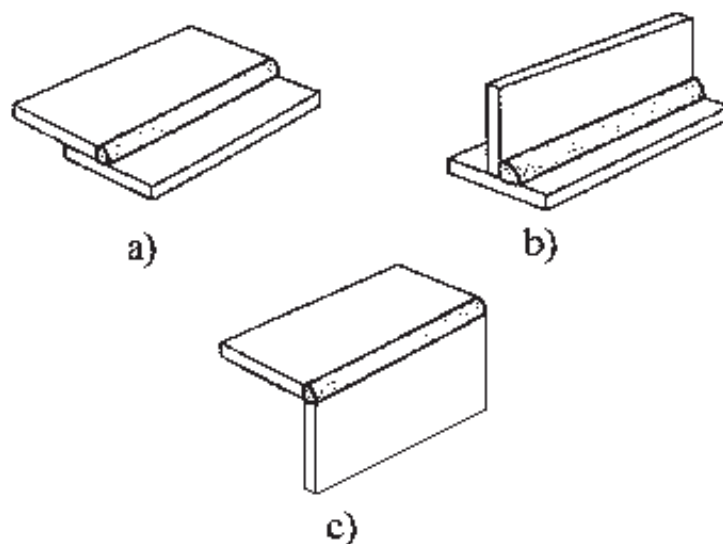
Soldaduras de filete: a) Traslape, b) En "T" y c) En esquina.
